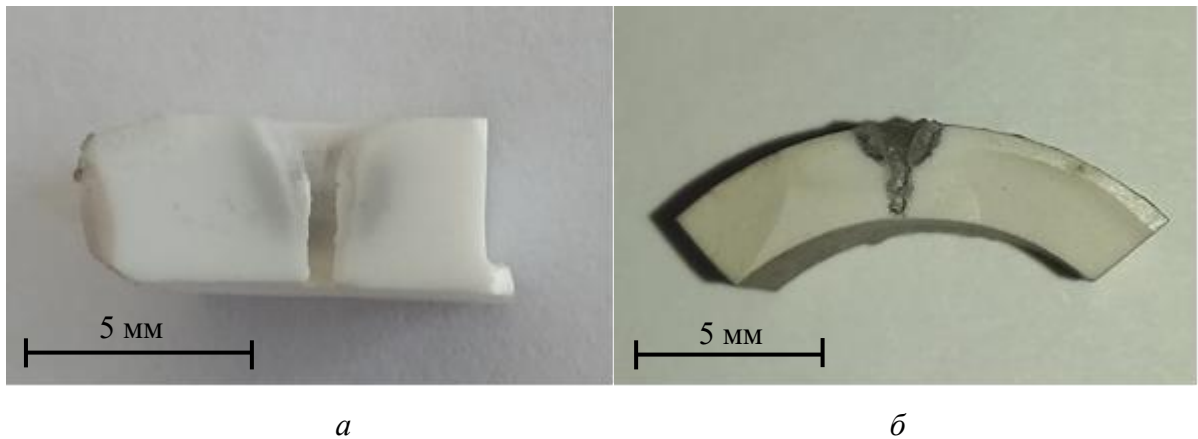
Пример электронно-лучевой фрезеровки кварцевой пластины
